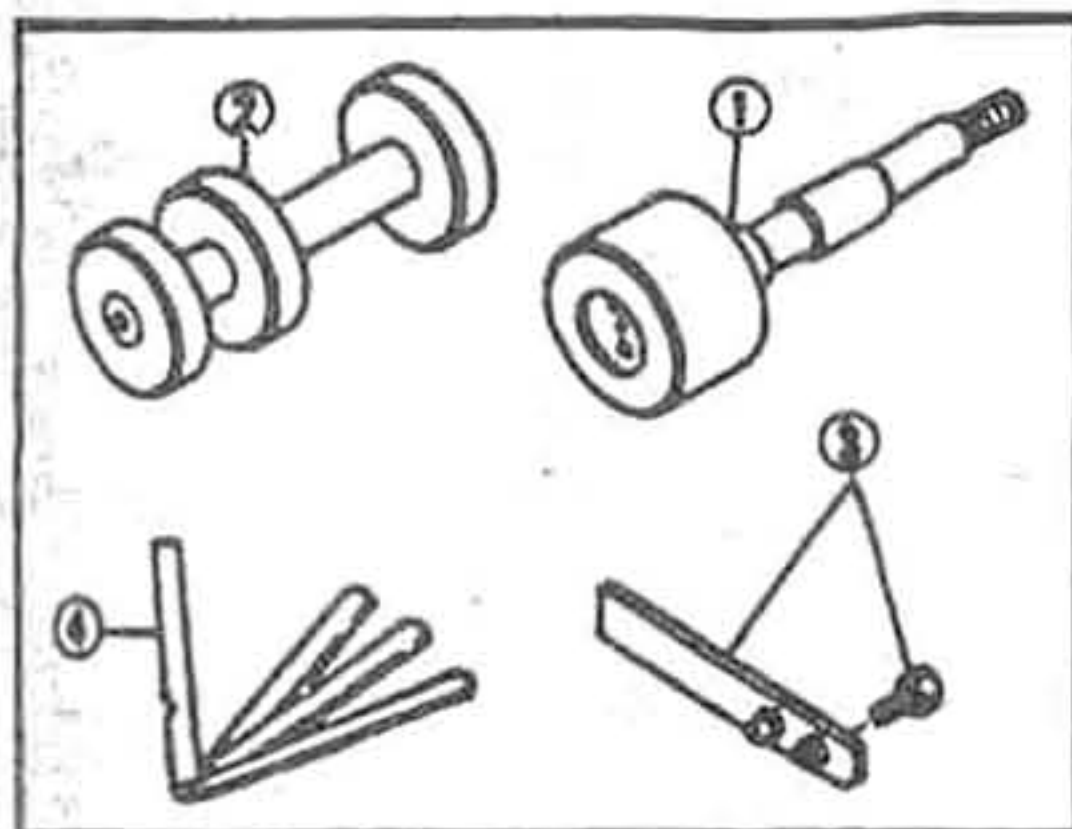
1. Измеритель высоты типа KV-381-03910. 2. Промежуточный вал KV-381-00120. 3. Фиксатор KV-381-00140. 4. Набор щупов.
